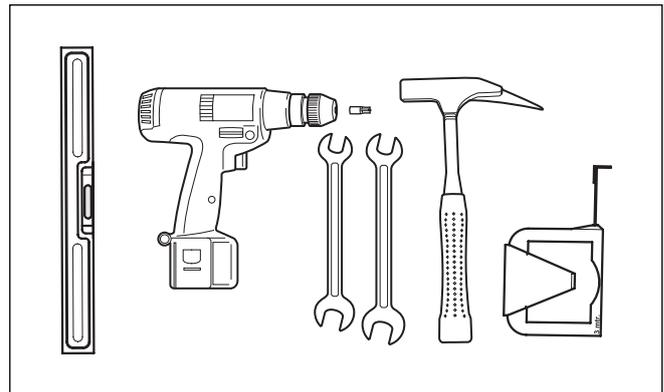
Montage-Werkzeuge: Wasserwaage, Akku-Schrauber, Torx-Bit (TX30, im Lieferumfang enthalten), Steck-/Maulschlüssel (SW 13), Hammer, Maßband/Gliedermaßstab
